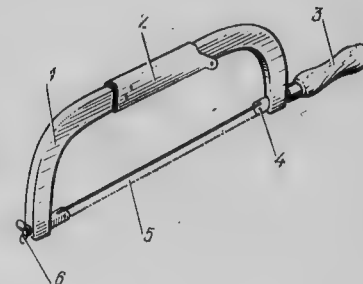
1 — колено составное с обоями; 2 — планка соединительная; 3 — ручка; 4 — держатели; 5 — полотно ножовочное; 6 — гайка-барашек
